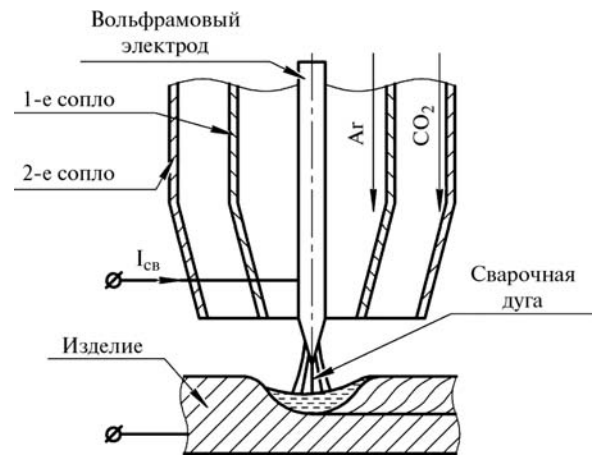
Схема процесса сварки неплавящимся электродом
